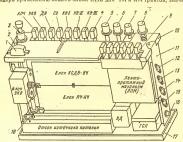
Схема расположения основных узлов в деталей на шасся магнитолы «Ореанда 301»:
